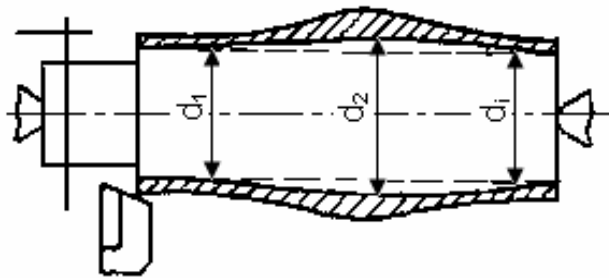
«Копіювання» форми заготовки в поздовжньому напрямку
